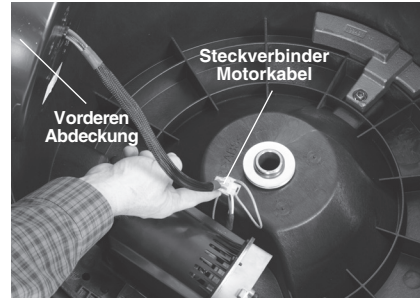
Geöffnetes Gehäuse der Rohrreinigungsmaschine
